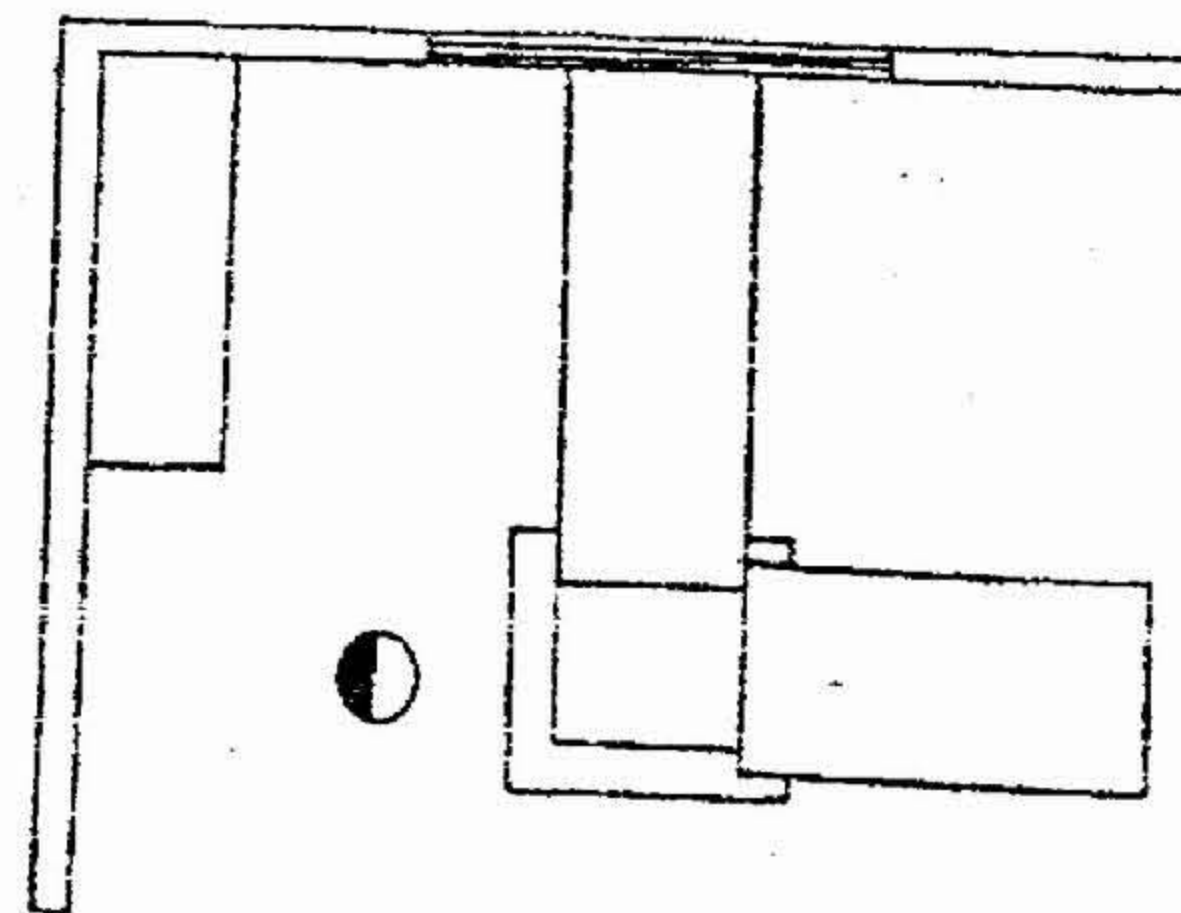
Рабочее место слесаря-инструментальщика для проковки и правки пил:
